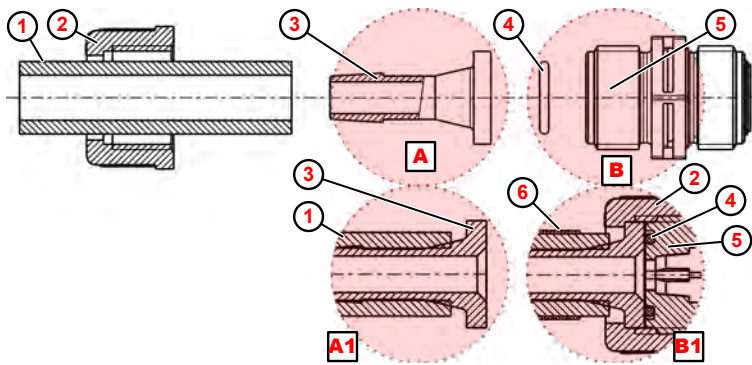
Raccord de conduit et flexible avec embout et collier de serrage
